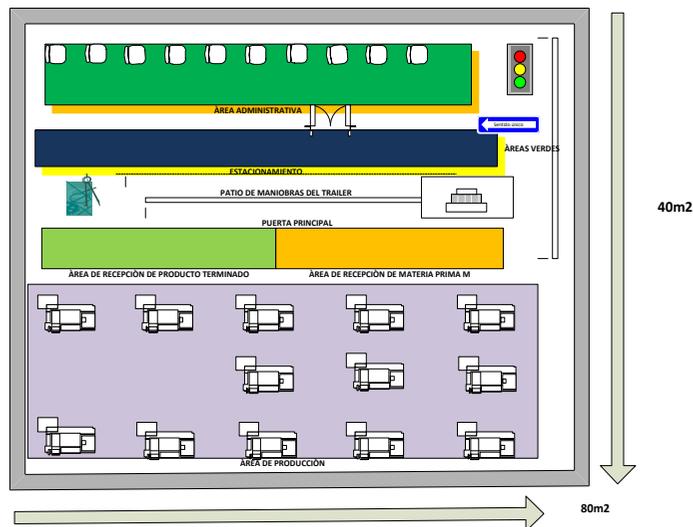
FIGURA IV.XVI PLANTA CON 13 MÁQUINAS
